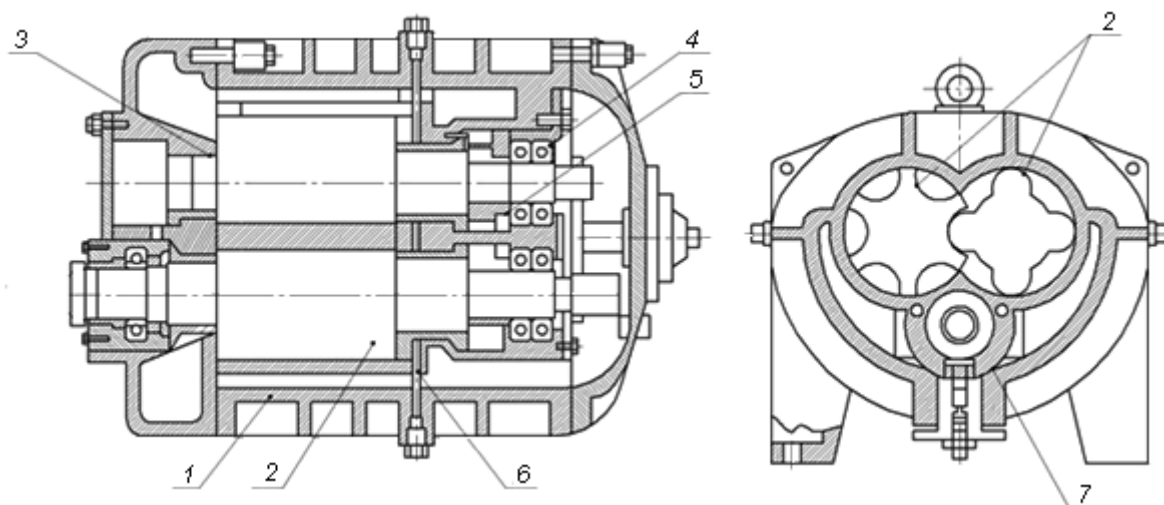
Общий вид винтовой компрессорной установки: 1 — корпус компрессора; 2 — роторы компрессора; 3 — подшипники скольжения; 4 — радиально-упорные шарикоподшипники; 5 — разгрузочный поршень; 6 — сменная торцевая подставка
